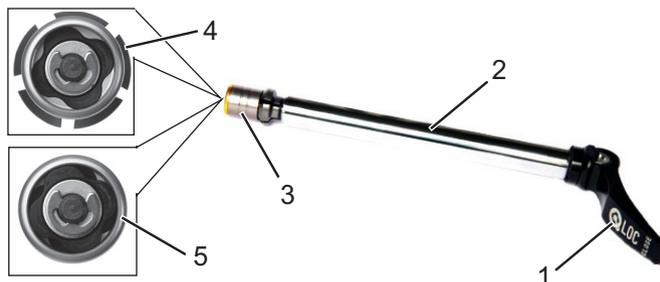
Attache rapide, modèle II, avec levier de serrage (1), axe (2), écrou de réglage (3) et vue détaillée de la bride ouverte (4) et fermée (5)
